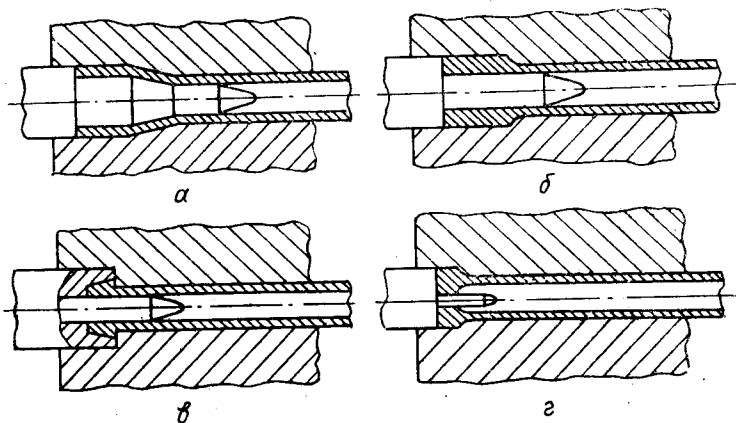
Висаджування потовщень різної форми на трубчастих заготовках.
